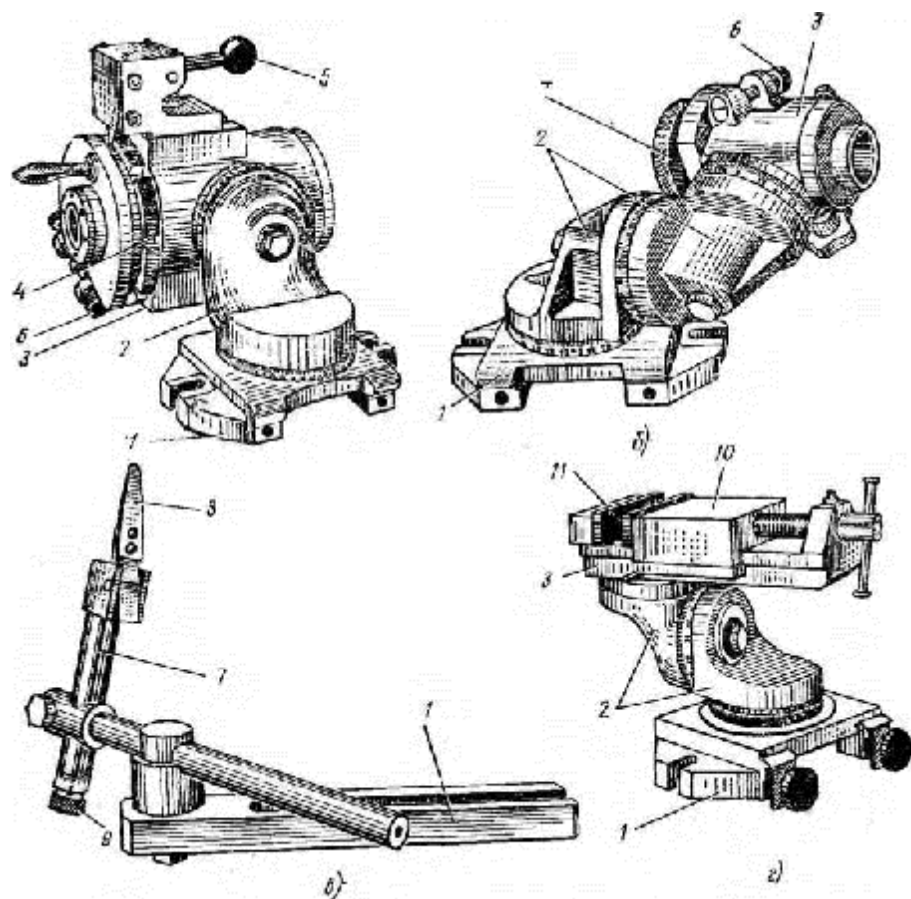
Пристосування до універсально-заточувального верстата.
